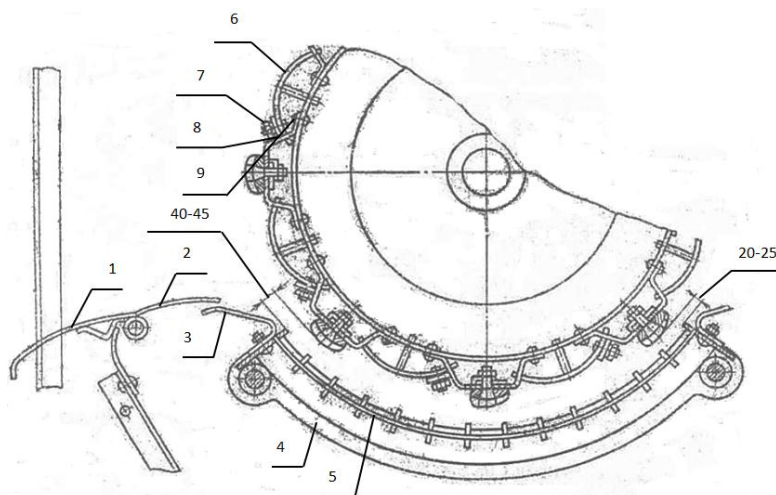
Подготовка молотильного аппарата к уборке кукурузы на зерно: 1 – фланг; 2 – направляющая; 3 – козырек; 4 – подбарабанье; 5 – пруток; 6 – шпилька; 7 – гайка; 8 – упор; 9 – щиток.
